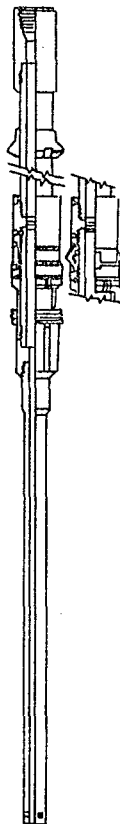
Herramienta soldadora tipo "C" ó "C-2"
